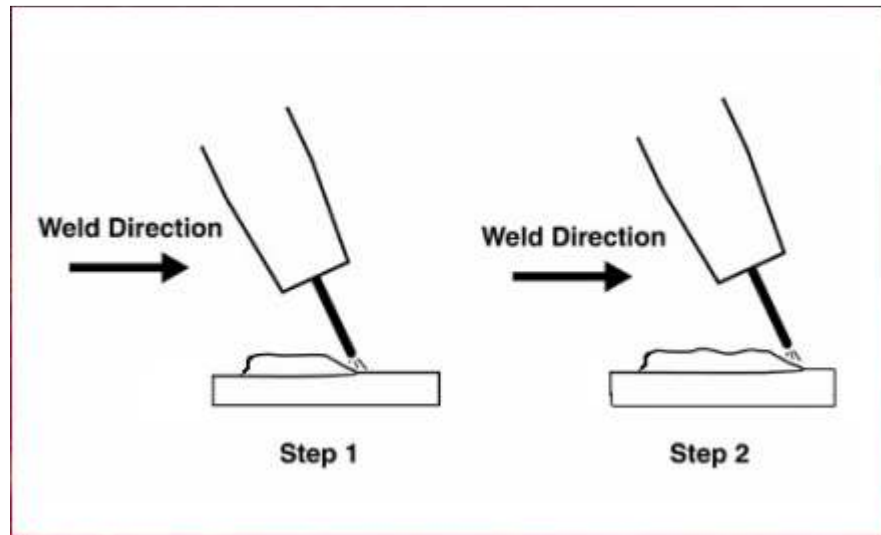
Técnica de Inicio de la soldadura para el Proceso MIG-MAG. Lincoln Soldaduras de Colombia, presentación (2007). p. 32.
